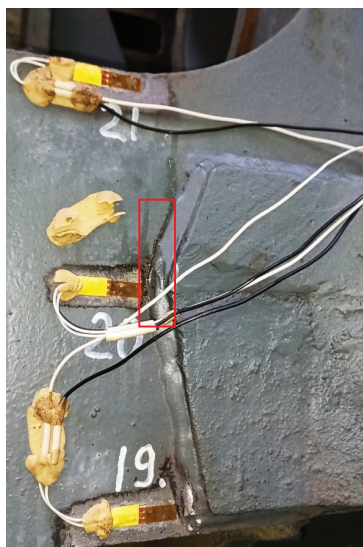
Внешний вид трещины № 2 на боковине № 2
